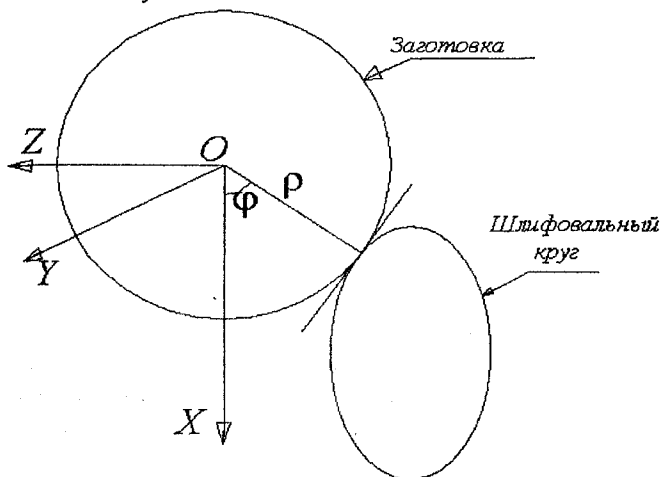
Контакт шлифовального круга и обрабатываемой заготовки в сечении $y = \text{const}$
